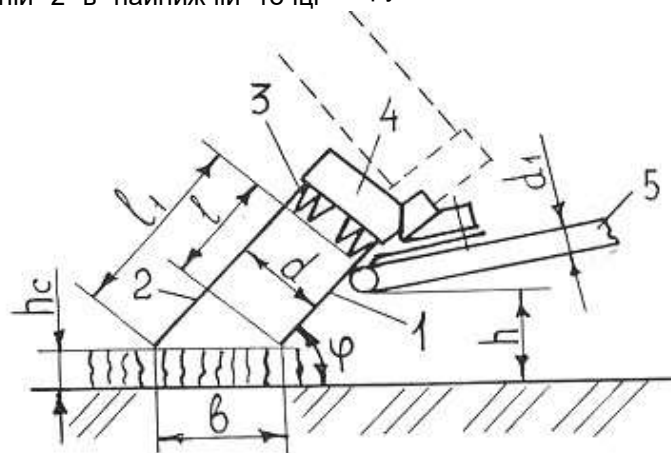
Схема відцентрових робочих органів ротора машини: 1 і 2 - внутрішній і зовнішній палець грабліни; 3 - грабліна; 4 - поворотня обойма; 5 - обід ротора
